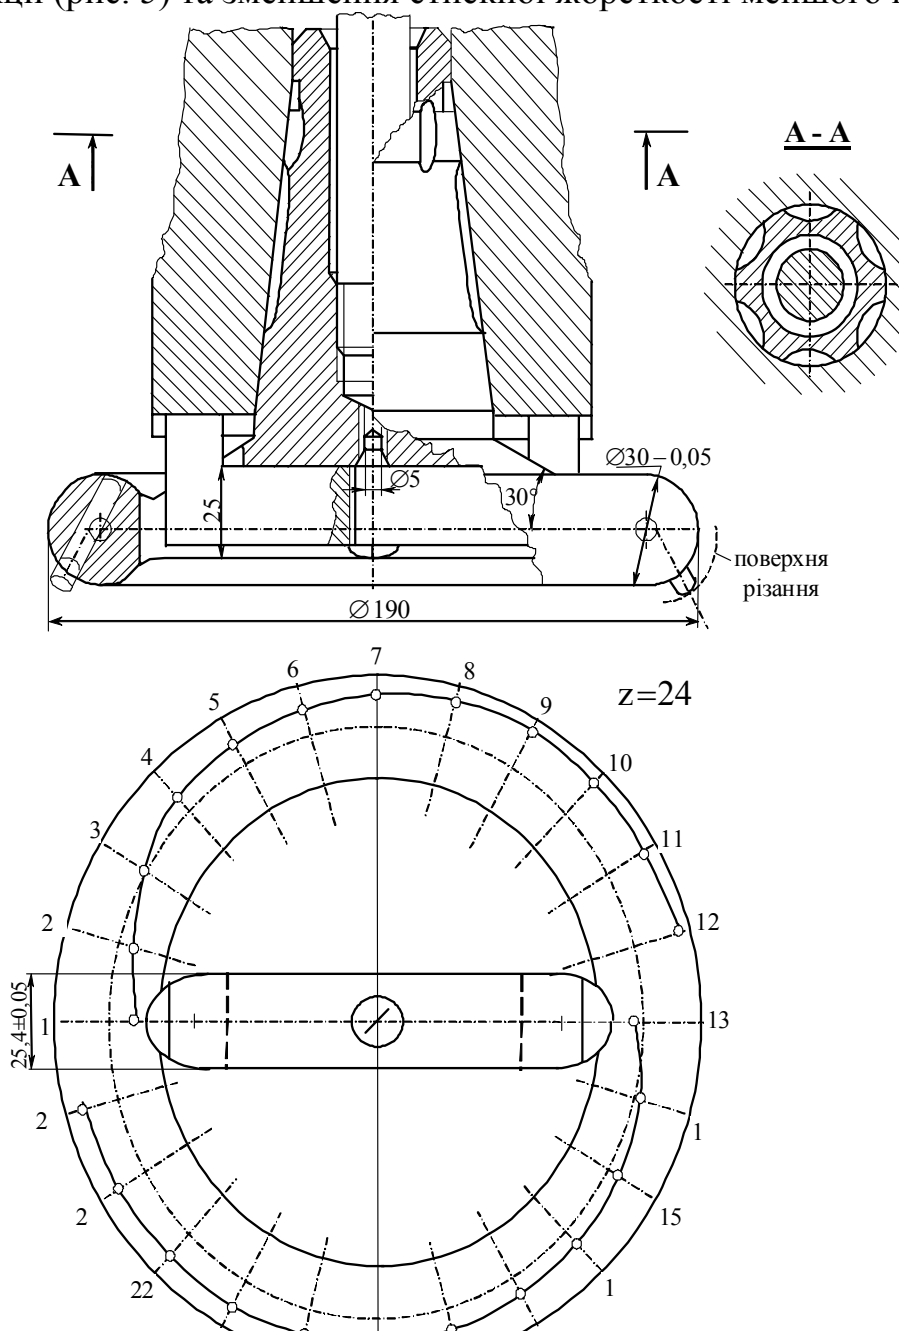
Конструкція фрези в з'єднанні зі шпинделем верстата
